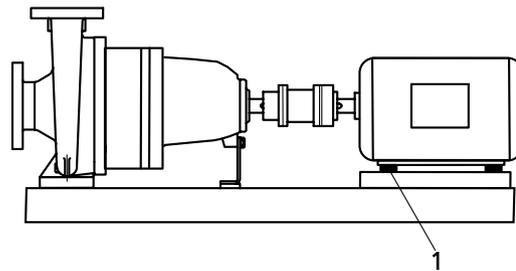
Pumpenaggregat ohne Stellschrauben ausrichten
